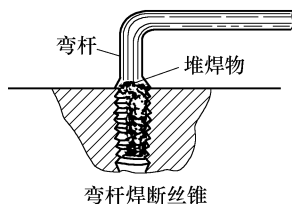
焊接弯杆或螺母取出断丝锥法
